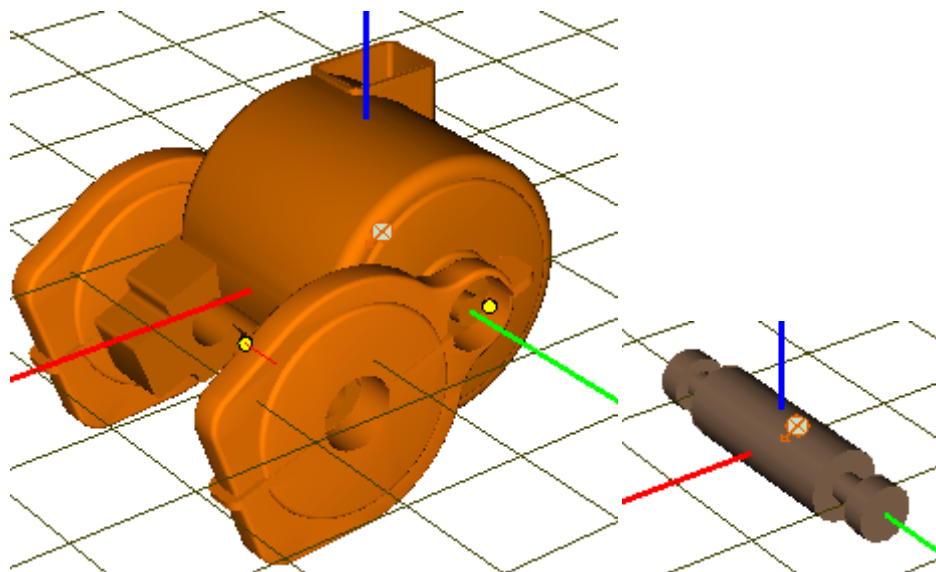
Тела: корпуса тягового двигателя и редукторов и ротор
